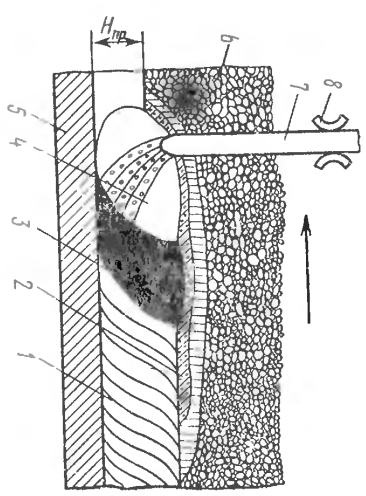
Схема дуговой сварки под флюсом:
